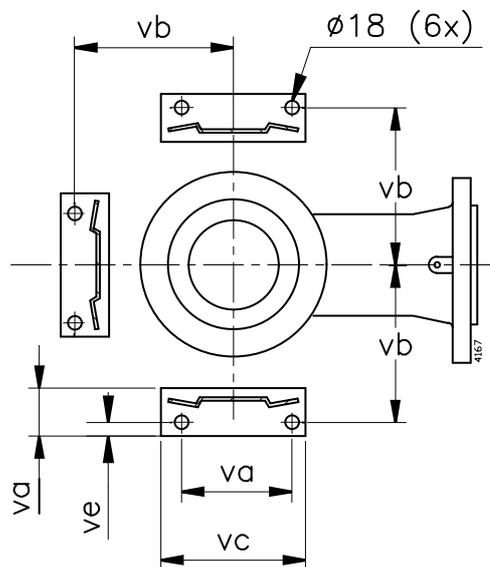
Abmessungen der Fußpads (Draufsicht).
